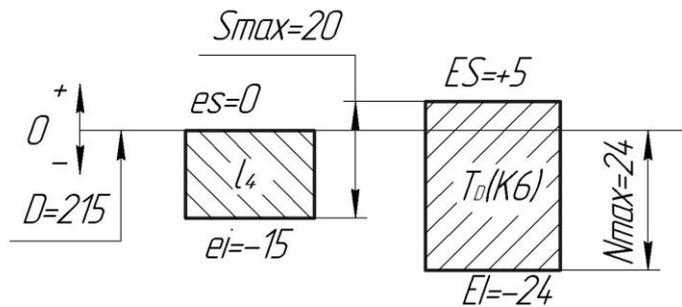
Схема розташування полів допусків зовнішнього кільця підшипника в корпусі
